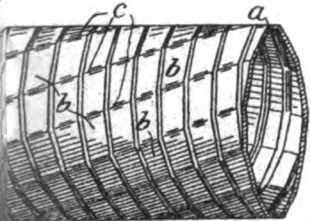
Schlauch mit mehrgängigem Gewinde.
